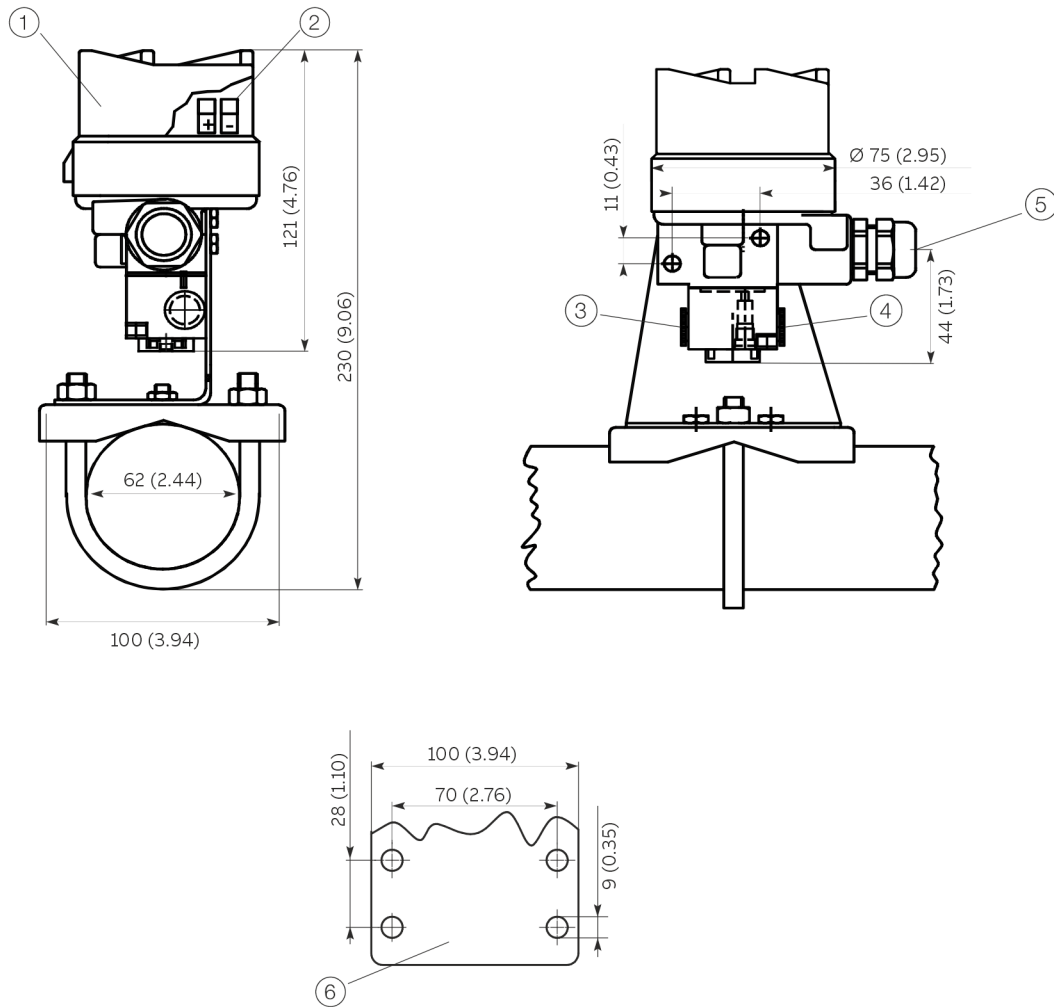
Dimensiones de diseño de carcasa de control para montaje en regleta
